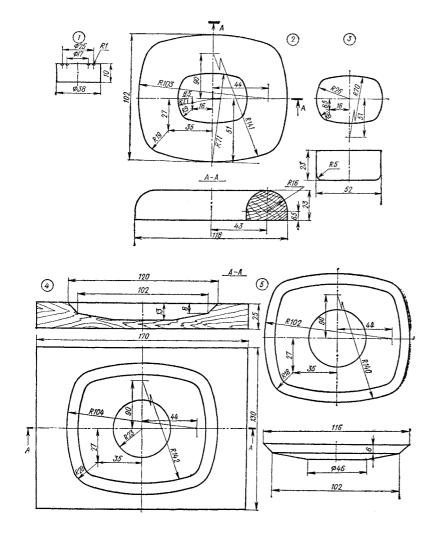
Эскизы приспособления для изготовления телефонов. 1 — матрица для изготовления центрирующей шайбы, текстолит; 2 — модель амбушюра, дерево; 3 — пуансон, дерево; 4 — матрица для штамповки коробки, дерево; 5 — пуансон для штамповки коробки, дерево.
